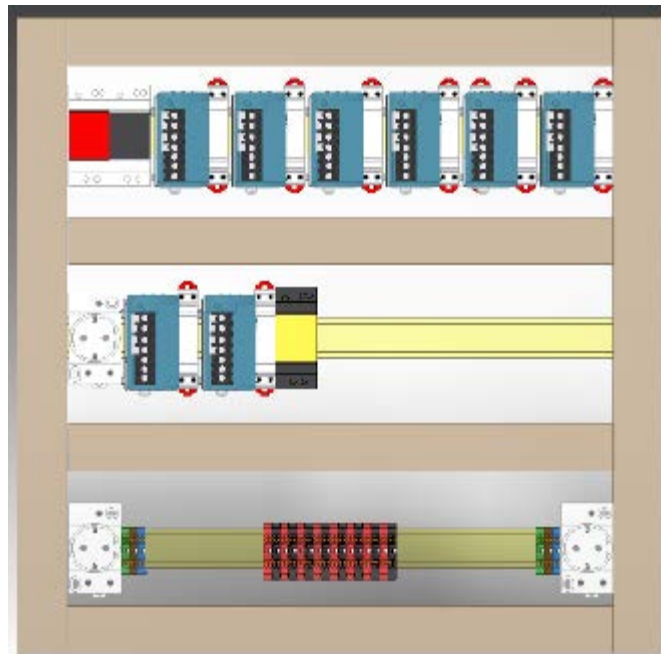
Vista superior o de planta del modelo 3D de la plancha.
